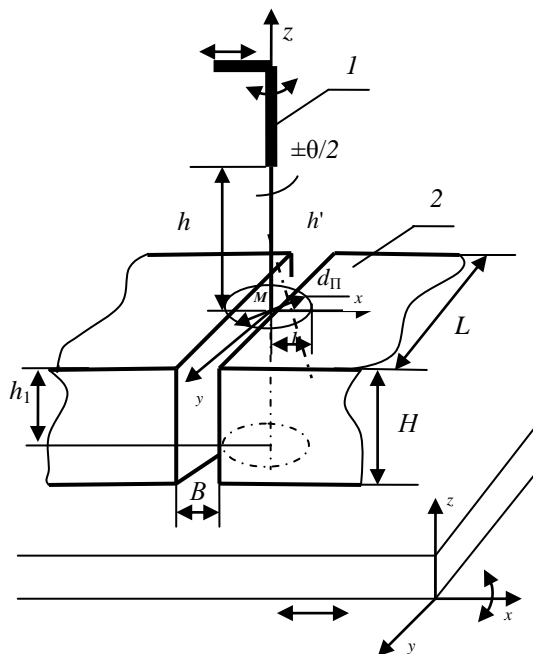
Положение фокального пятна нагрева ЭЛ на поверхности стыка с учётом конструктивных характеристик стыкового соединения: где d_{Π} – диаметр ЭП; h – расстояние от среза сварочной пушки до плоскости сварного шва (длина ЭП); h' – длина отклонённого на угол θ ЭП; H – толщина свариваемых изделий; l – смещение центра пятна нагрева M при отклонении оси ЭЛ от перпендикулярности; M – центр пятна нагрева ЭЛ; h_1 – глубина проплавления; L – длина сварного шва; B – ширина зазора в стыке; 1 – ЭЛП; 2 – свариваемое изделие.
